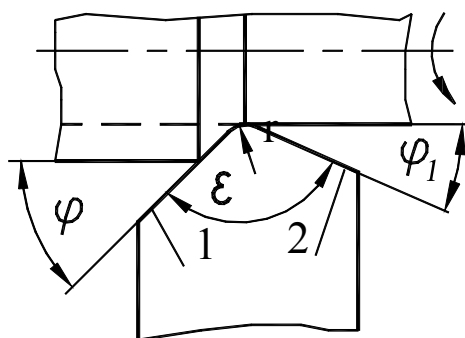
Геометрические параметры лезвия резца в основной плоскости: 1 – главная режущая кромка; 2 – вспомогательная режущая кромка; φ – главный угол в плане; φ_1 – вспомогательный угол в плане; ϵ – угол при вершине; r – радиус при вершине
